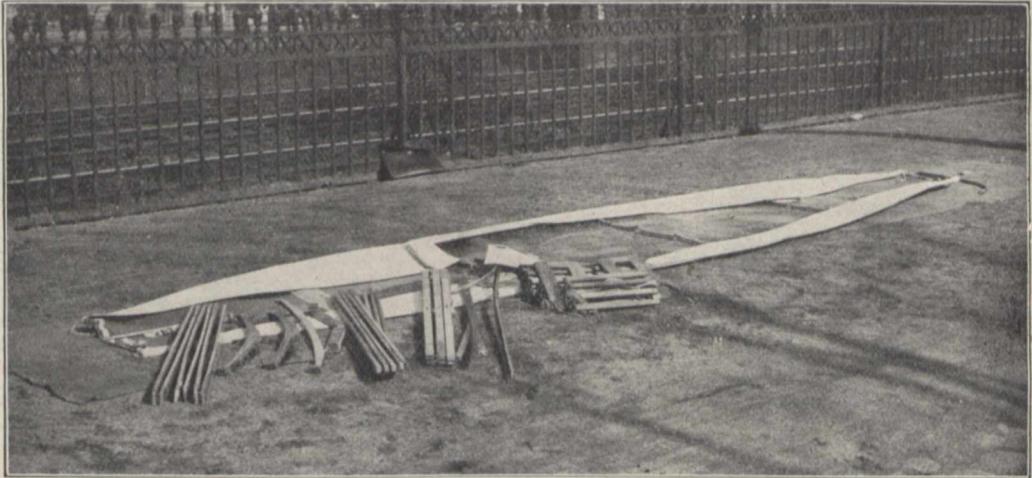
Einzelteile des Rollbootes, wie Sitze und Holzleisten.
